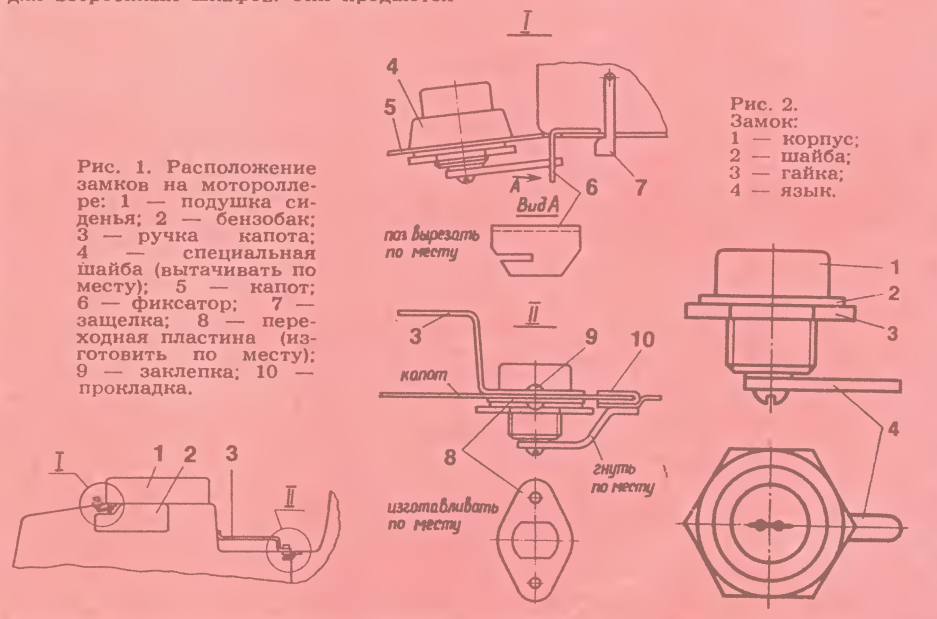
Расположение замков на мотороллере: 1 — подушка сиденья; 2 — бензобак; 3 — ручка капота; 4 — специальная шайба (вытачивать по месту); 5 — капот; 6 — фиксатор; 7 — защелка; 8 — переходная пластина (изготовить по месту); 9 — заклепка; 10 — прокладка.
